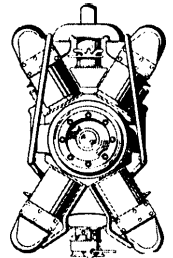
X-förmiger Motor (1 Kurbelwelle). Typ Packard 1 A 2775
